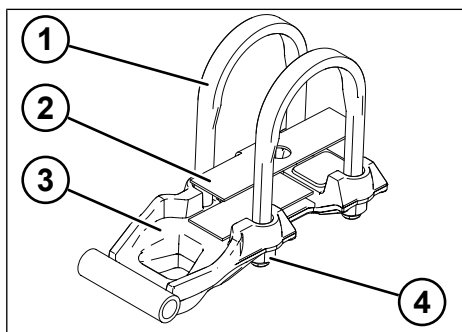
Компоненты соединительного элемента (нижний рычаг пневматической подвески)
